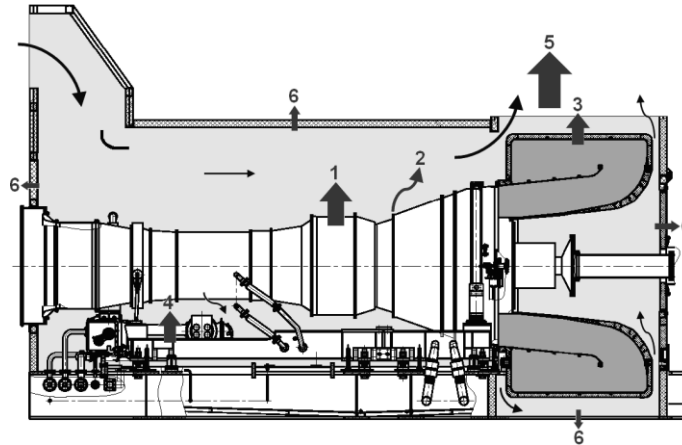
Схема теплового баланса укрытия ГТУ:
